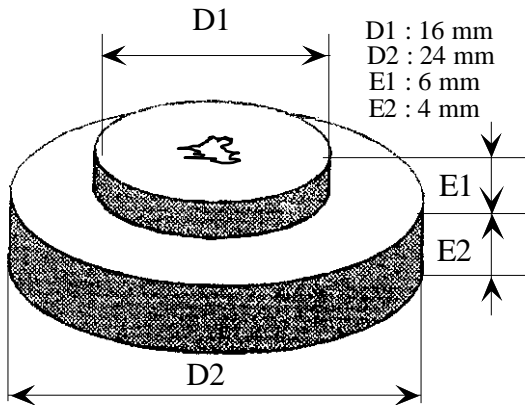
Dimensions principales de l'éprouvette plane.
